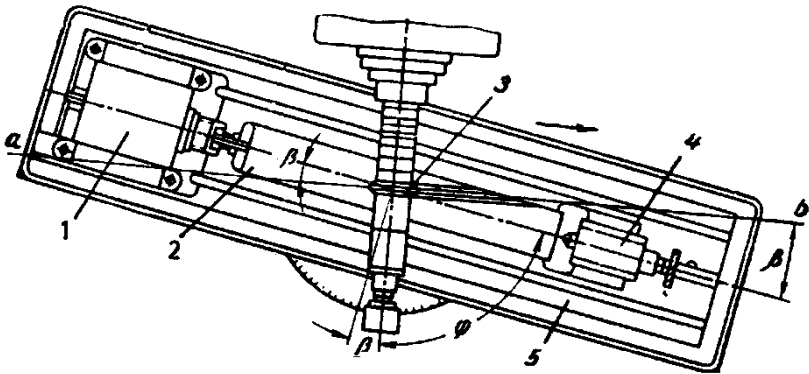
Установа стола для фрезерування гвинтових канавок
